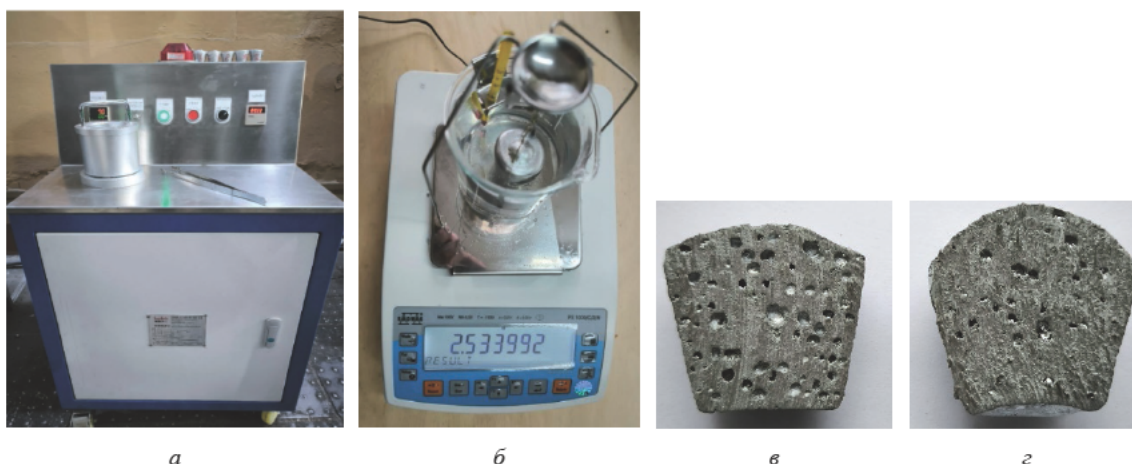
Оборудование для RPT-теста и образцы сплава: а – анализатор для RPT-теста; б – весы лабораторные для определения плотности образца; в – образец сплава для анализа до проведения металлургической обработки; г – образец сплава для анализа после металлургической обработки и фильтрации через ПКФ
